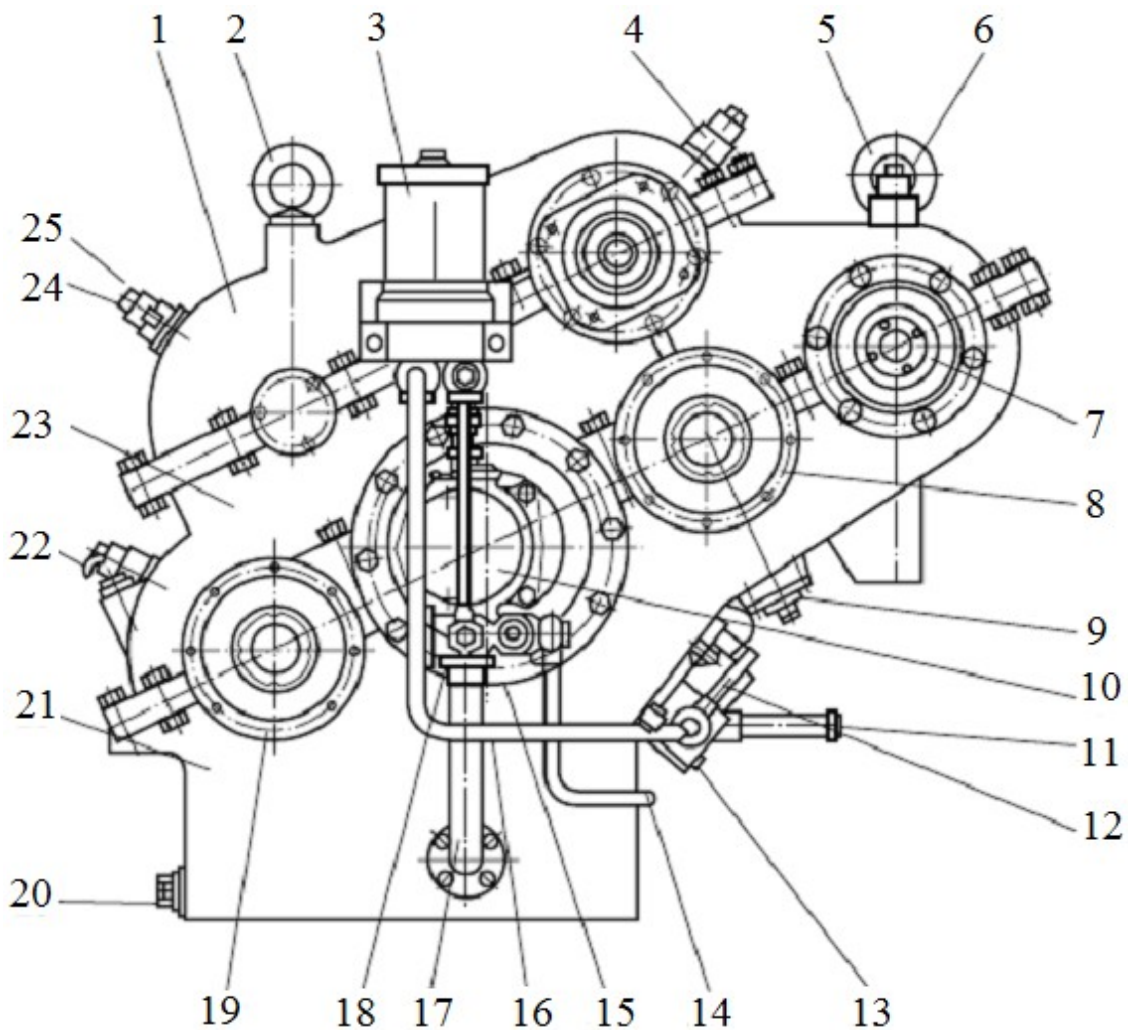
Гідромеханічна передача ГМП-300 (вигляд спереду): 1 – картер верхній; 2, 5 – рим-болти; 3 – фільтр; 4, 6, 25 – вимикачі кінцеві; 7 – вал привода компресора і генератора; 8 – вал вхідний; 9 – датчик індукційний; 10 – насос НШ-50-4; 11 – патрубок; 12, 14, 16, 17, 18 – трубопроводи; 13 – коробка клапанна; 15 – коробка клапанна вхідна; 19 – вал вантажний задній;
